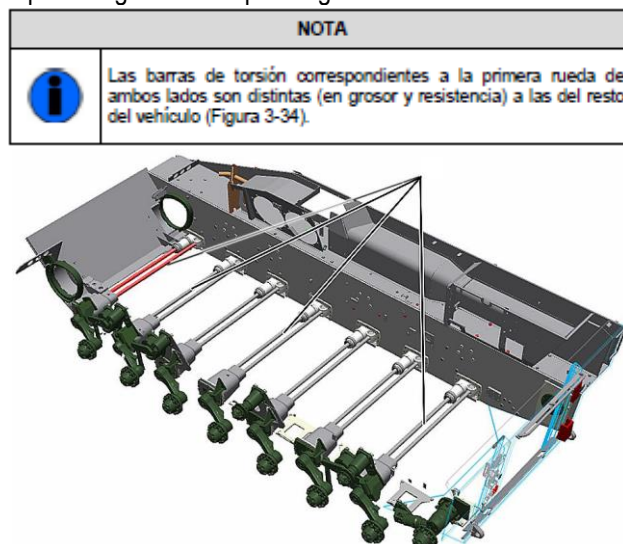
Barras de torsión VCI Pizarro fase 2. (MT-103 T1)
